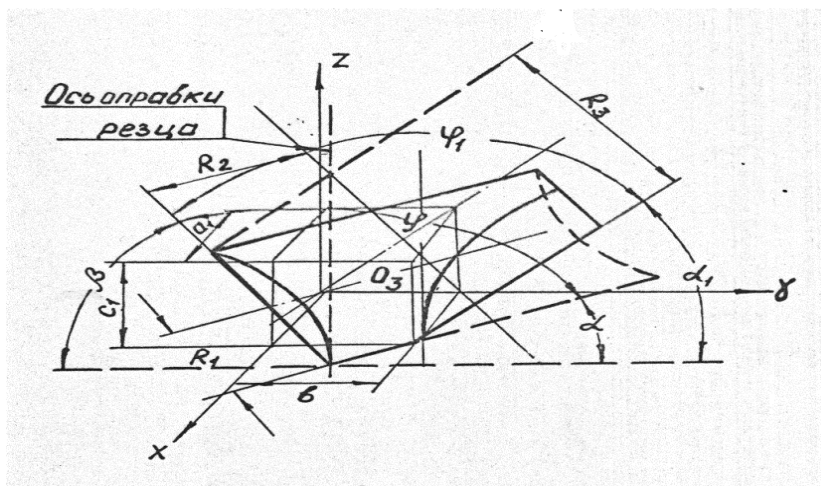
Расположение цилиндрических поверхностей, образующих лезвия резца трапецеидального профиля
